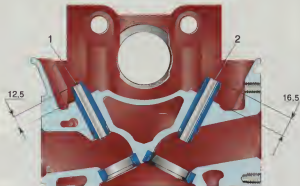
Положение направляющих втулок после запрессовки в головку блока: 1 – под маслоотражательный колпачок; 2 – штатная.
